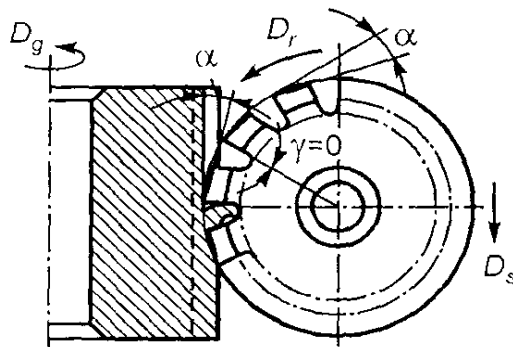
Схема обработки зубьев колеса червячной фрезой
